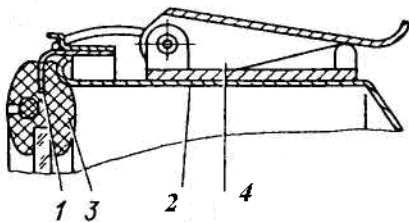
Патефонний замок: 1 – рамка; 2 – корпус; 3 – гумове кільце, що ущільнює; 4 – патефонний замок
